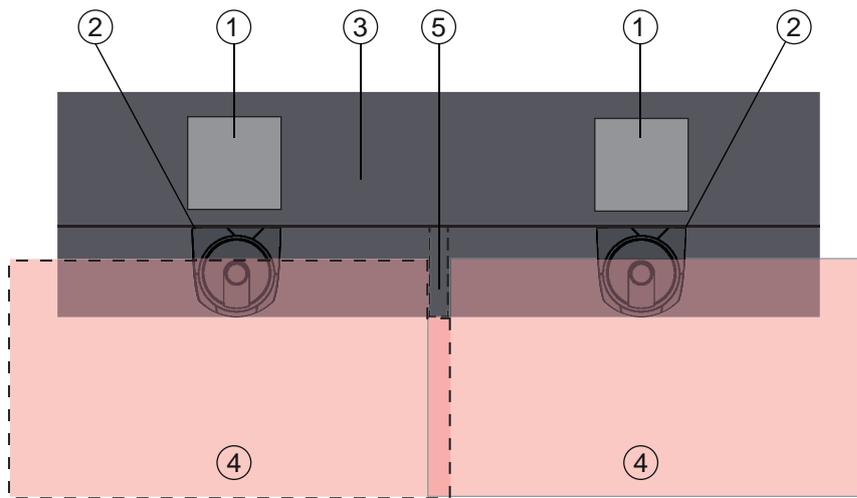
Hintertretschutz durch Einsenkung in die Maschinenkontur
